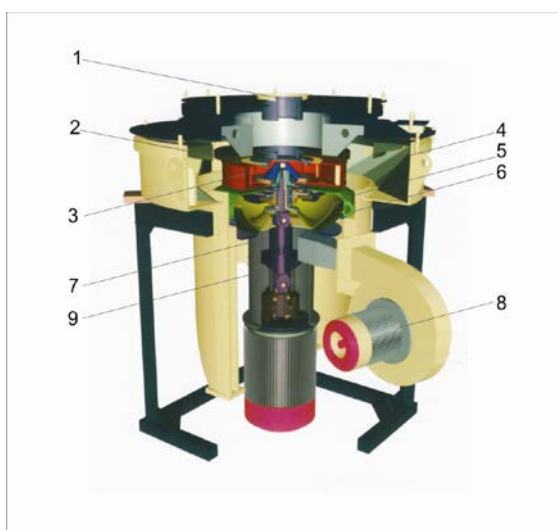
Центробежно-ударная дробилка ДЦ: 1 – воронка; 2 – камера дробления; 3 – распределительный конус; 4 – ускоритель; 5 – ротор; 6 – статор; 7 – камера, к которой создается воздушный зазор; 8 – вентилятор высокого давления; 9 – карданная передача.
